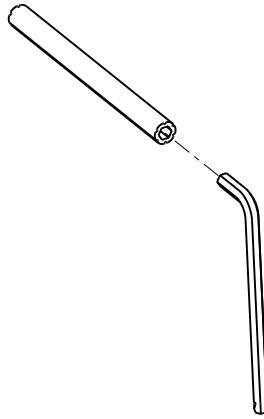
Sechskantschlüssel und Ausbauwerkzeug-Verlängerung
